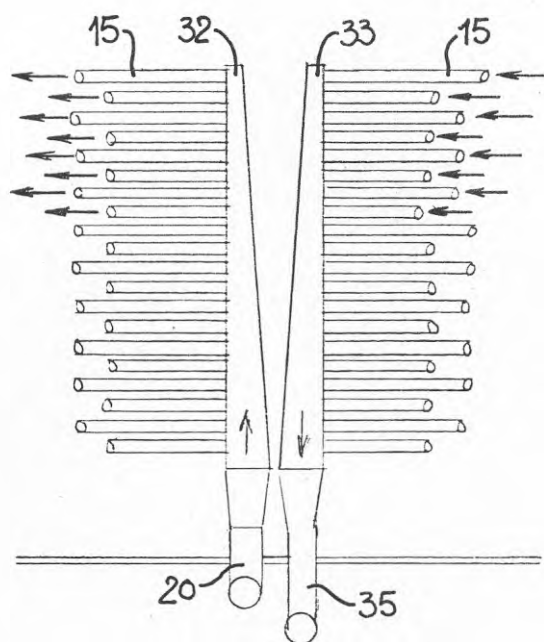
Värmeväxlarens konstruktion - detalj
